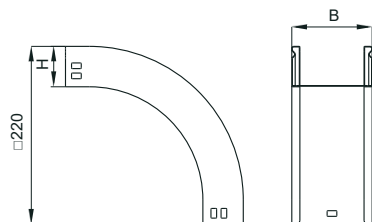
Поворот плавный на 90° вертикальный внешний / Figure B.2 – 90° vertical external smooth bend
